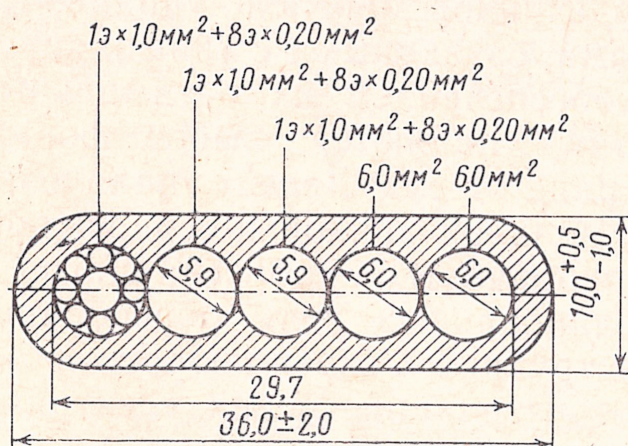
Схема конструкции плоского кабеля марки П-КУФР.
